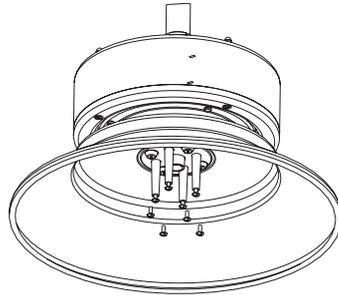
Forma de instalar la placa de montaje en la parte superior de la caja del interruptor
